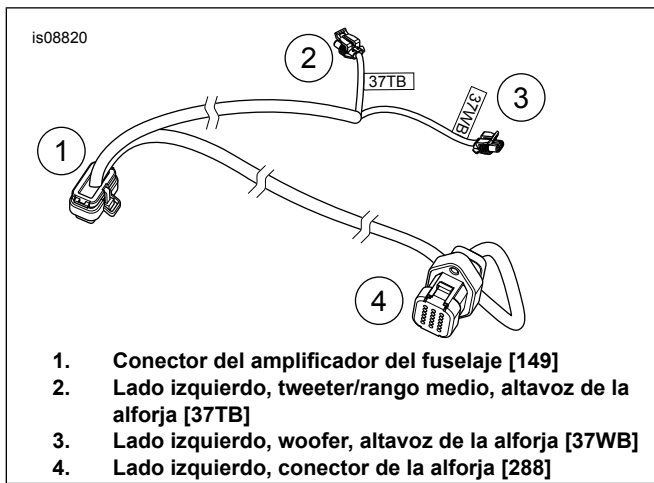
Arnés de cables, altavoz de la alforja del lado izquierdo
